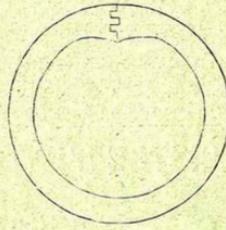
Tube à soudure à emboîtements, renforcée.
